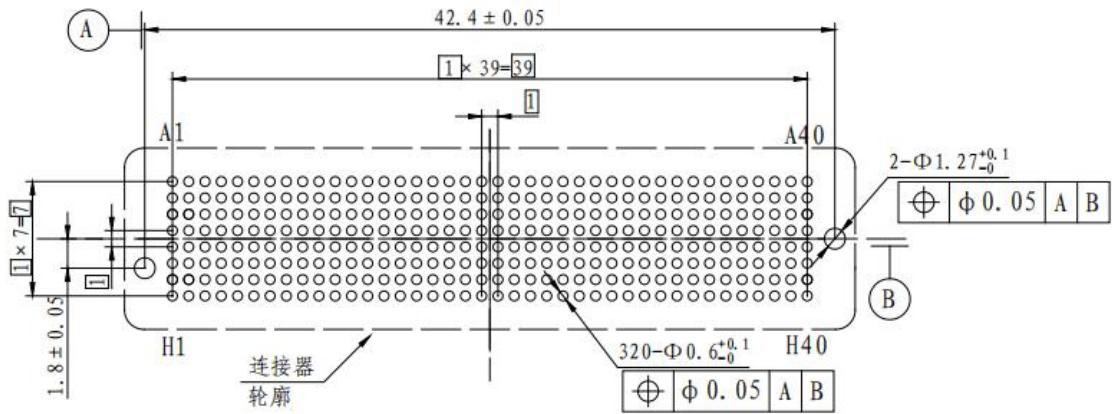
插座 PCB 开孔尺寸（从连接器安装面看）
